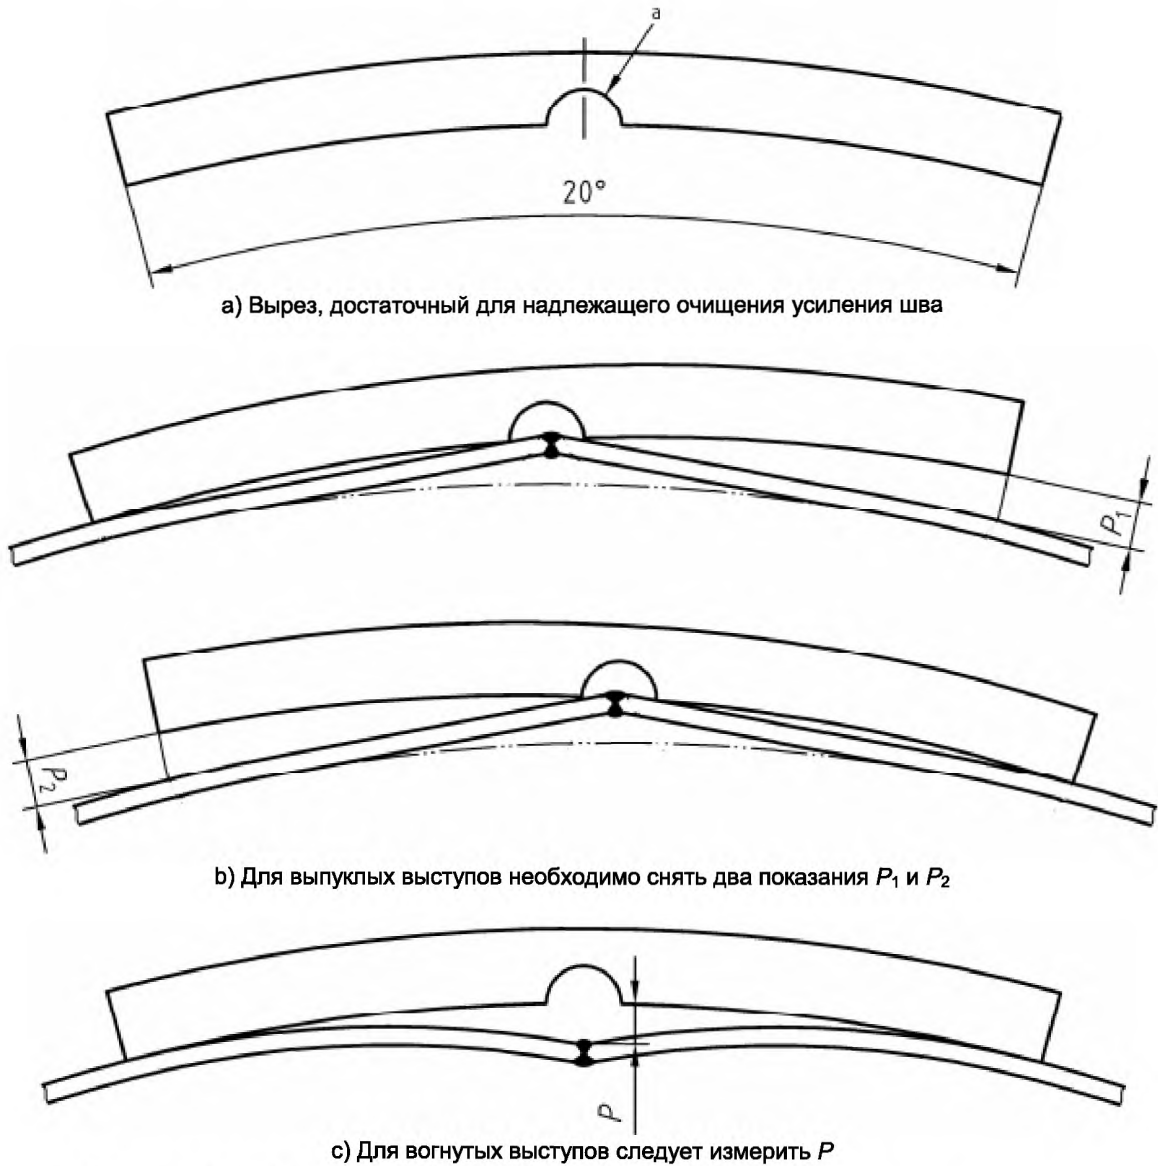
Детальный чертеж измерительного устройства, измерение выступов
